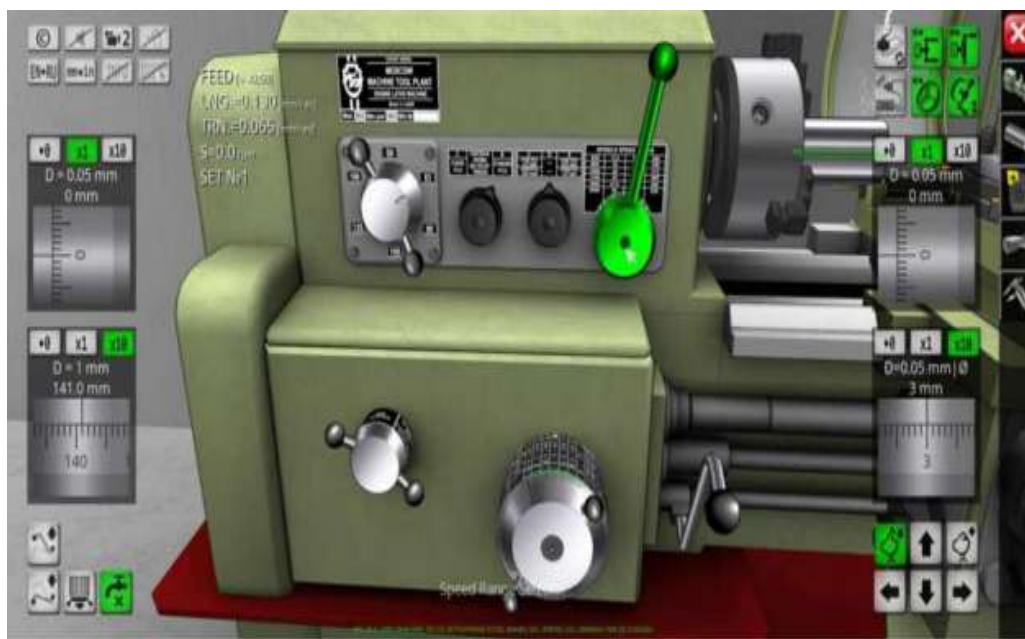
Области кликирования вокруг рукоятки джойстика механической подачи токарного станка
